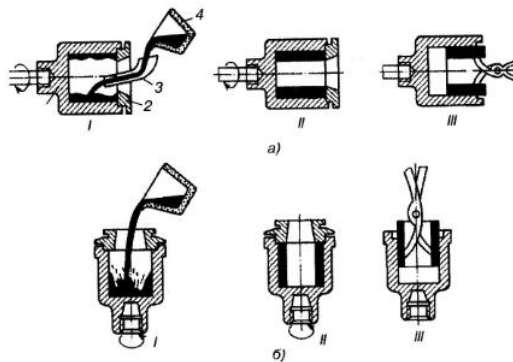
Схемы центробежного литья с горизонтальной (*a*) и вертикальной (*б*) осями вращения: *I* - заливка расплава во вращающуюся форму; *II* - формообразование отливки; *III* - извлечение отливки из изложницы; *I* - изложница; 2 - крышка; 3 - желоб; 4 - ковш
